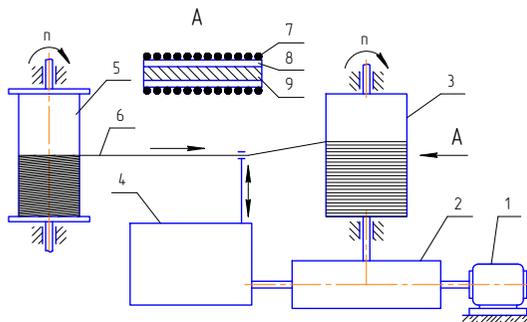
Схема намоточного приспособления для сборки заготовок типа «сэндвич»: 1 – электродвигатель; 2 – редуктор; 3 – оправка; 4 – укладчик волокон; 5 – катушка; 6 – армирующее волокно; 7 – армирующий элемент; 8 – матрица; 9 – оправка съемная
